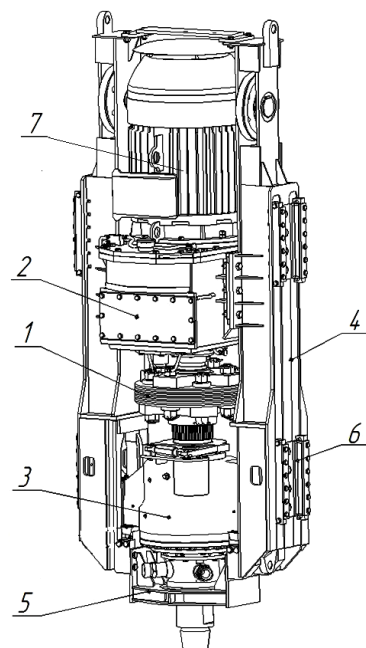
Головка бурового снаряда: 1 – муфта; 2 – редуктор вращателя; 3 – опорный узел; 4 – каретки с блоками; 5 – траверса; 6 – вкладыши полиуретановые; 7 – электродвигатель
